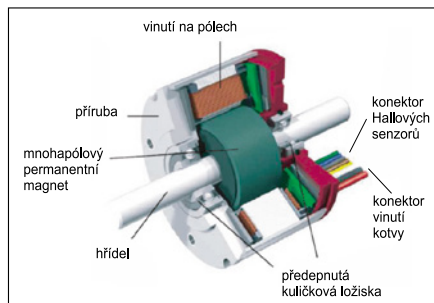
Řez válcovým EC motorem s vnějším rotorem, s vinutím na pólech
